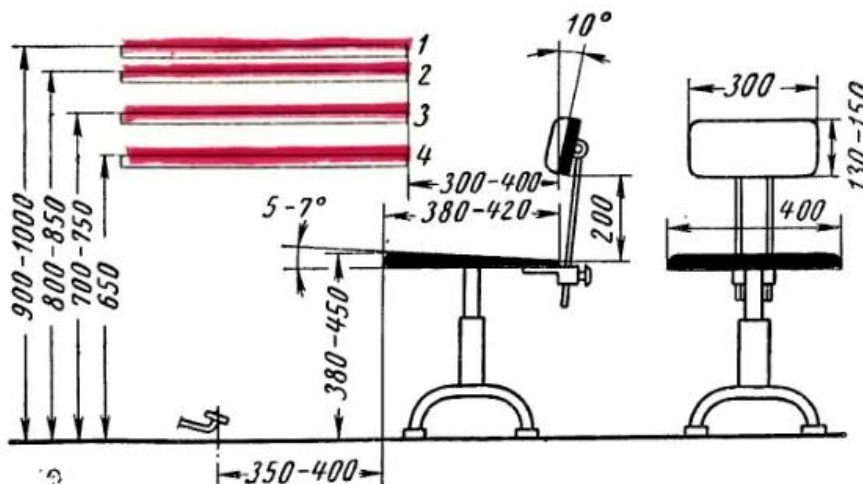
Основные размеры рабочего стула и рабочего сиденья обычного типа и правильные значения высоты рабочих поверхностей для основных видов работ
